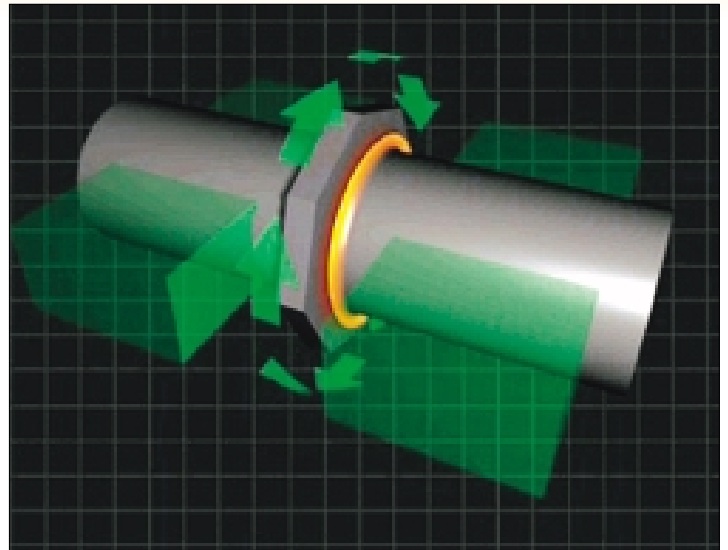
Principe de la nouvelle variante du procédé de soudage par friction
